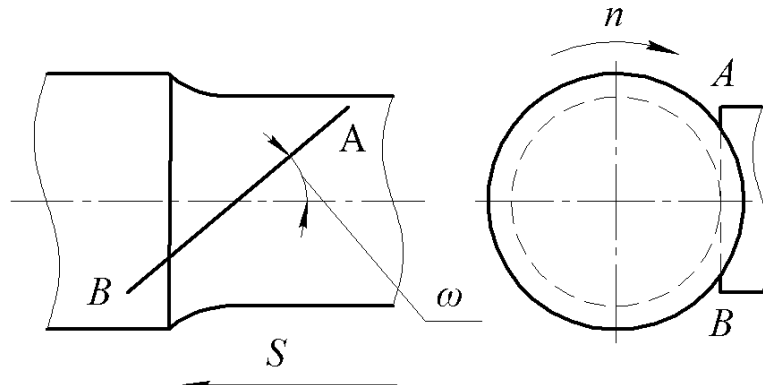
Схема работы безвершинного резца с прямолинейной режущей кромкой (AB – режущая кромка, S – подача, n – направление вращения заготовки, ω – угол наклона режущей кромки)
